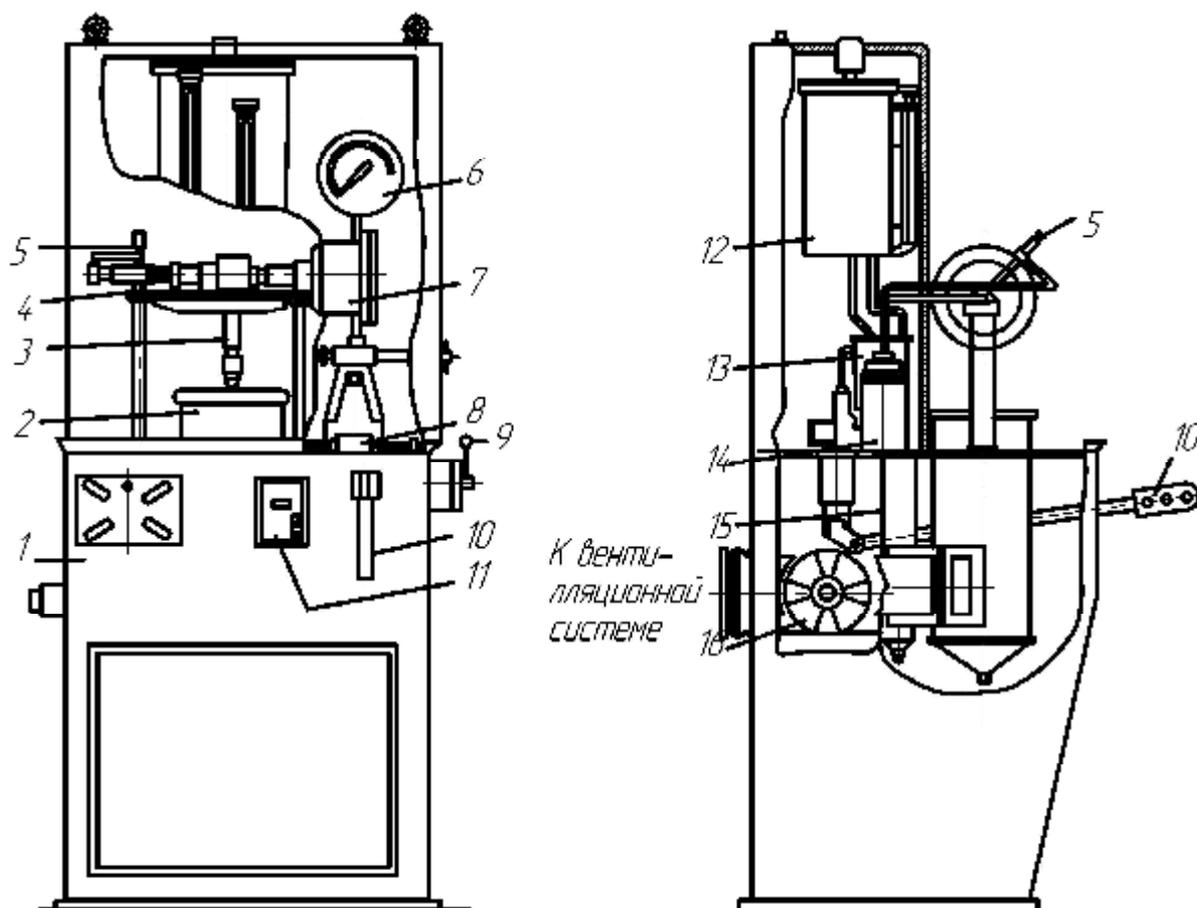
Стенд А106 для проверки работы форсунок ДВС: 1 – стол; 2 – сборник; 3 – проверяемая форсунка; 4 – зажимное устройство; 5, 9 – краны; 6 – манометр; 7 – пневмоцилиндр; 8 – топливный насос; 10 – ручка насоса; 11 – выключатель; 12 – топливный бак; 13 – фильтр; 14 – промывочный аккумулятор; 15 – отстойник; 16 – вентиляционный патрубок
